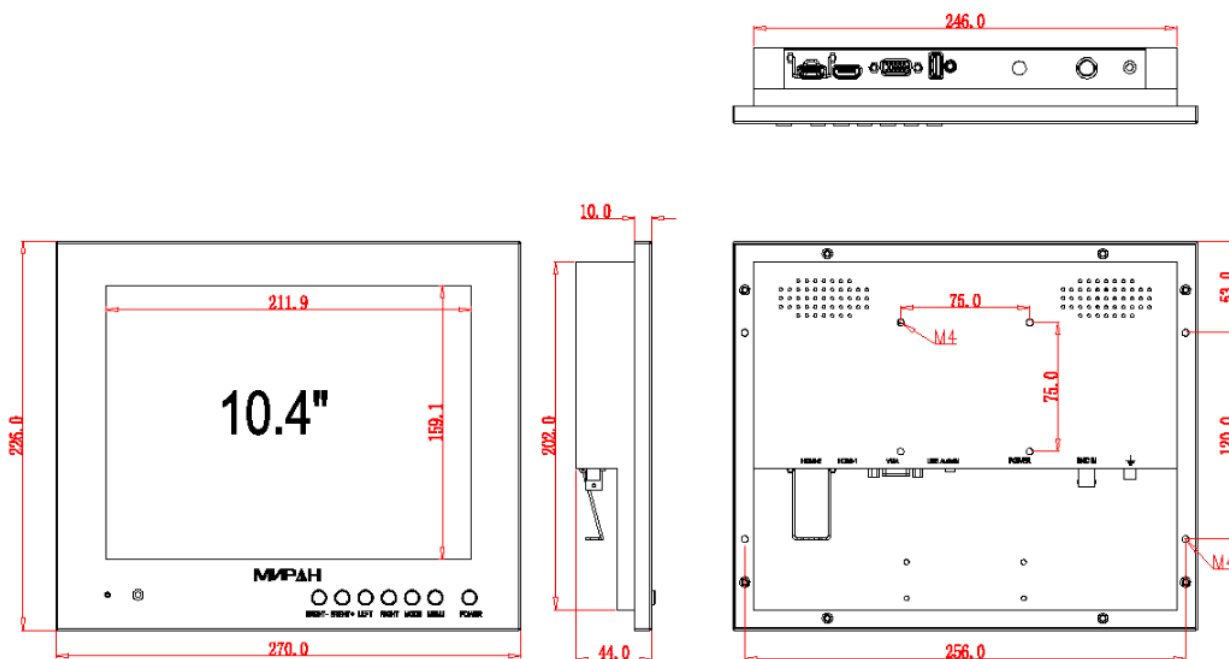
Габаритный чертеж монитора ИВМ-10ЖК.
